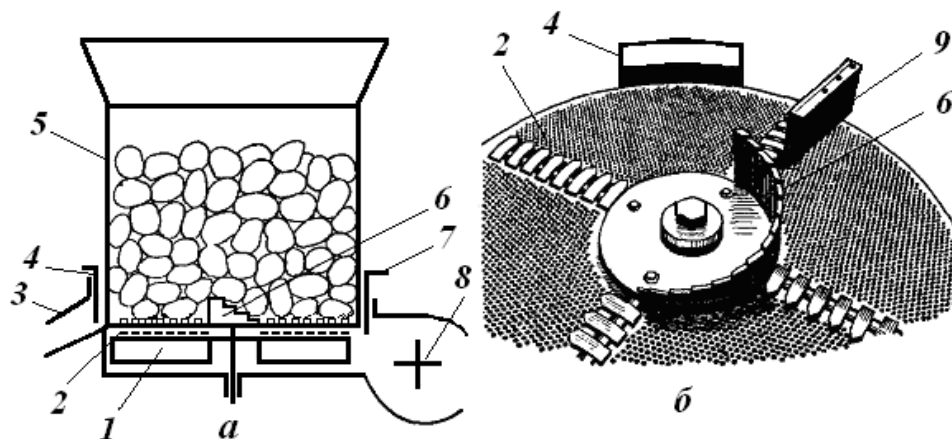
Подрібнювач-змішувач добрив ИСУ-4: а - функціональна схема; б - робочий орган; 1 - вивантажувальні лопаті; 2 - решето; 3 - потік; 4 - заслінка для вивантажування домішок; 5 - бункер; 6 - подрібнювач; 7 - заслінка для вивантажування добрив; 8 - ротор; 9 - шибер
